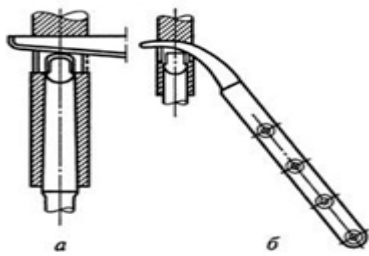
Клинья для удаления инструмента из шпинделя станка: а – плоский клин; б – радиусный клин
